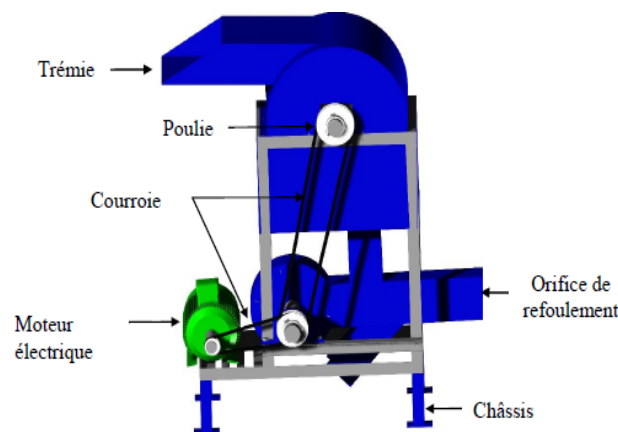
Dessin d'ensemble de l'égousseuse d'arachide
